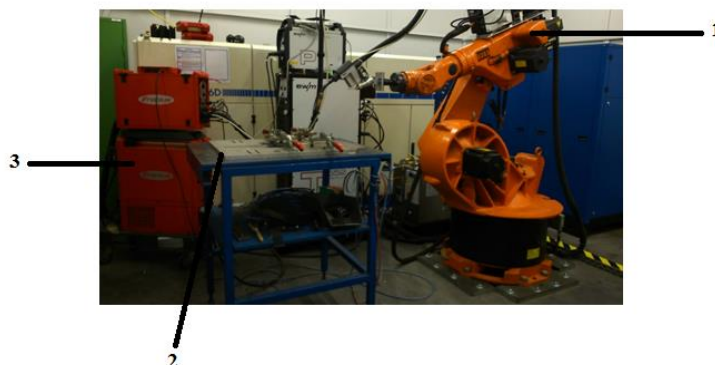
Сварочное оборудование СМТ, 1-сварочный робот «Кукa», 2-сварочный стол, 3-сварочная установка
